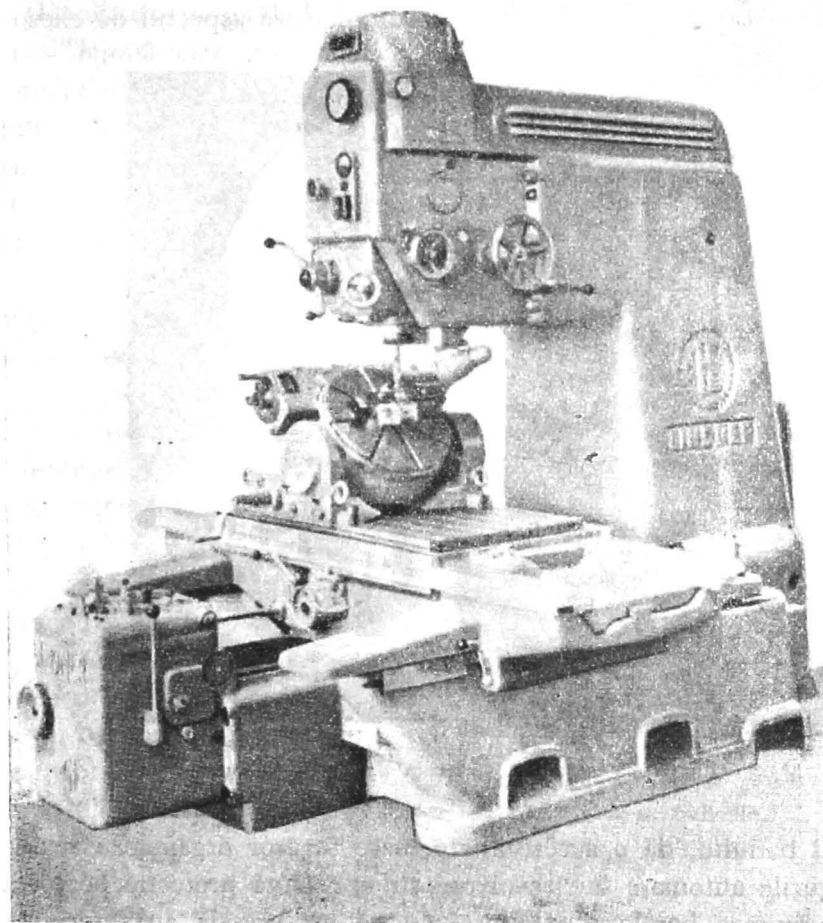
Mașină de găurit pentru dispozitive Lindner.
